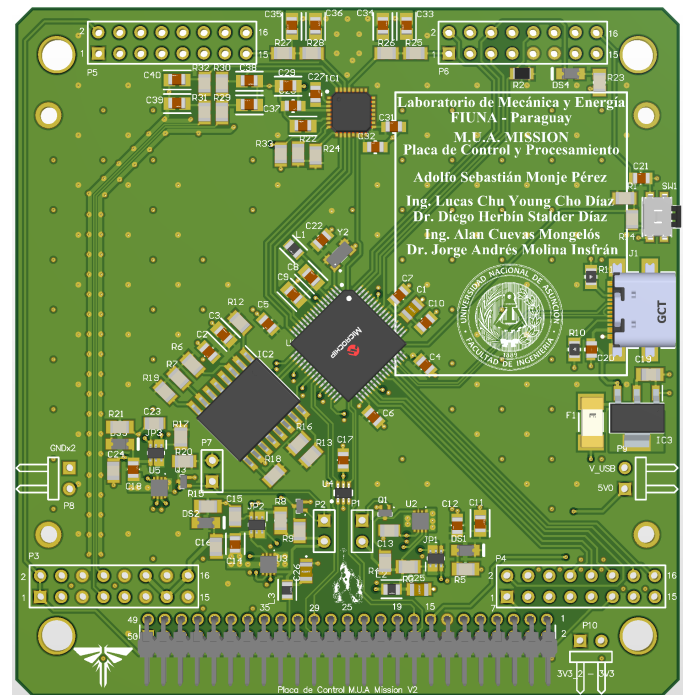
Vista frontal de la PCB diseñada. Fuente: Elaboración propia.
